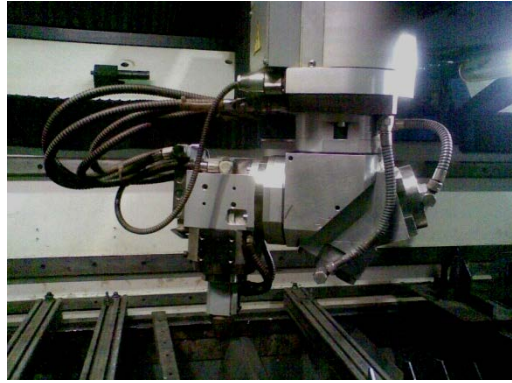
Lazer kaynaklı birleştirme için geliştirilen tutucu kaynak aparatı.
